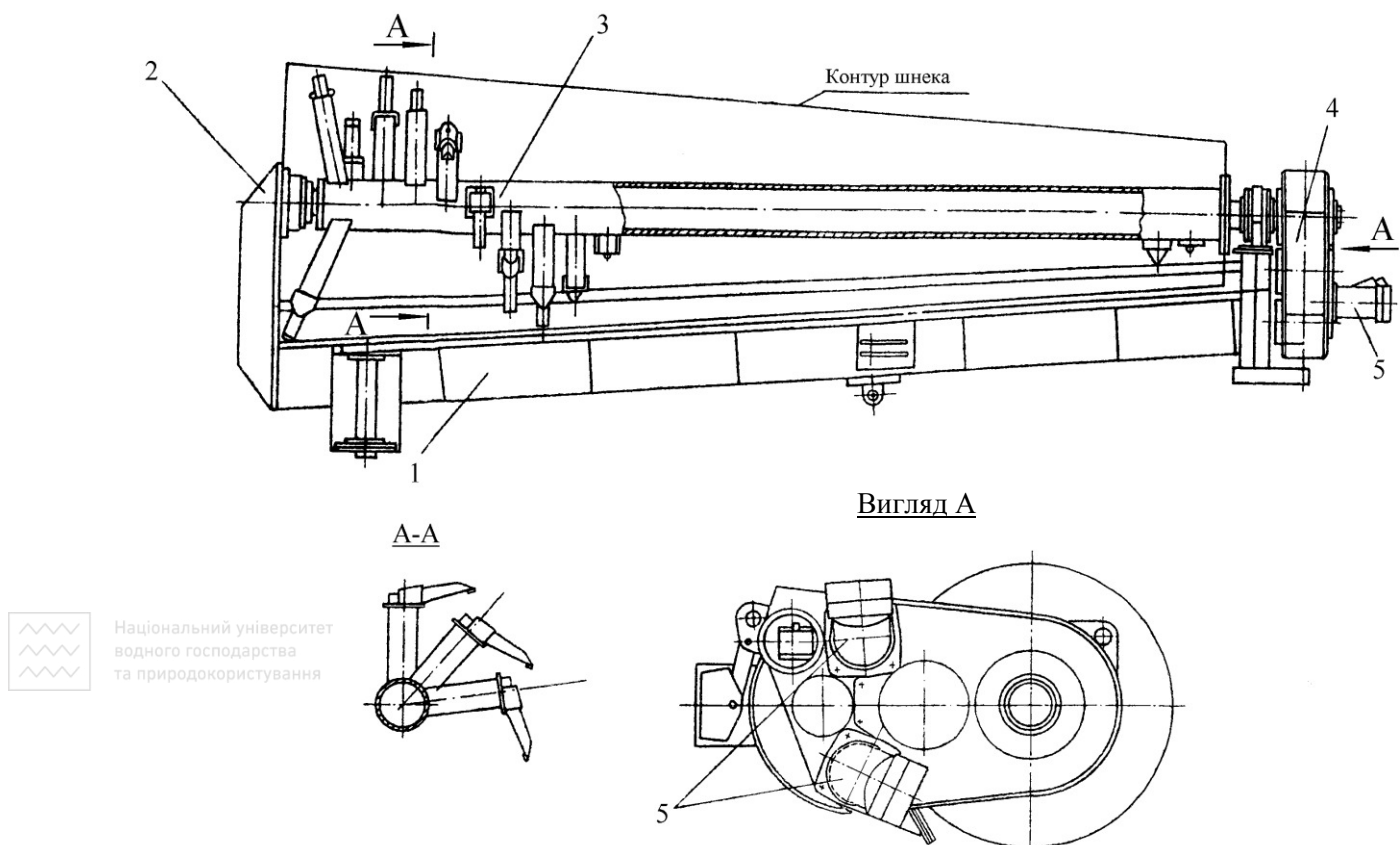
Конструкція шнека: 1 - зачисне обладнання; 2 - рама; 3 - шнек; 4 - редуктор привода шнека; 5 - гідромотори привода шнека
